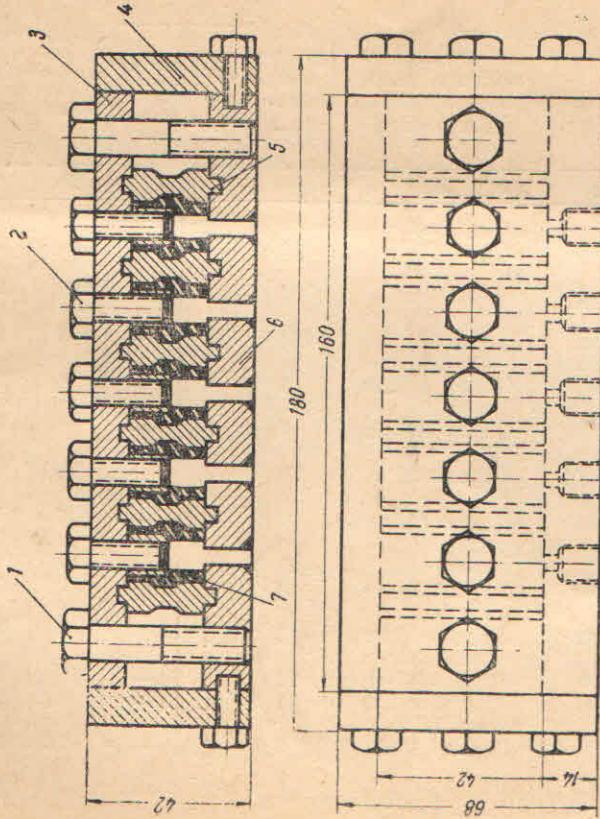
Пресс-форма в сборе с деталью № 30—6106086 — буфер ограничителя двери:
